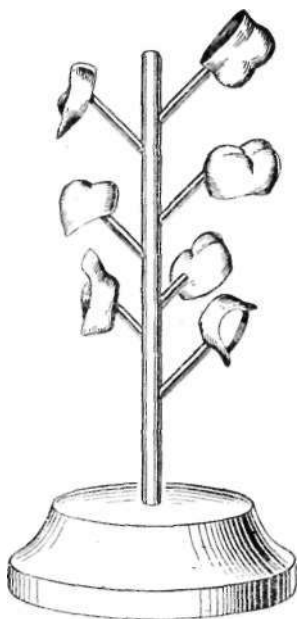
Расположение литникообразующих штифтов при отливке нескольких деталей.
